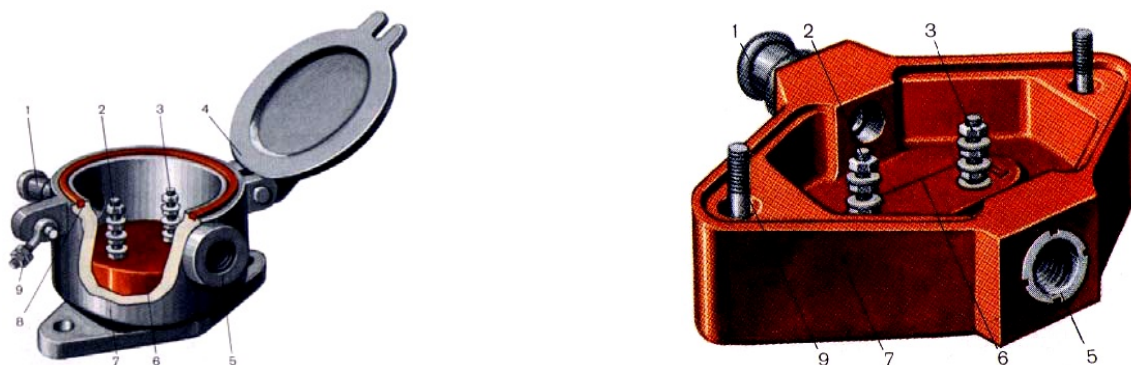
а,б. Двухтрубные клеммные коробки.
